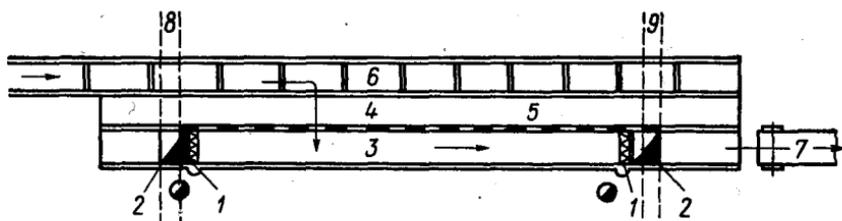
Расположение торцовочного стола с двумя торцовочными станками
